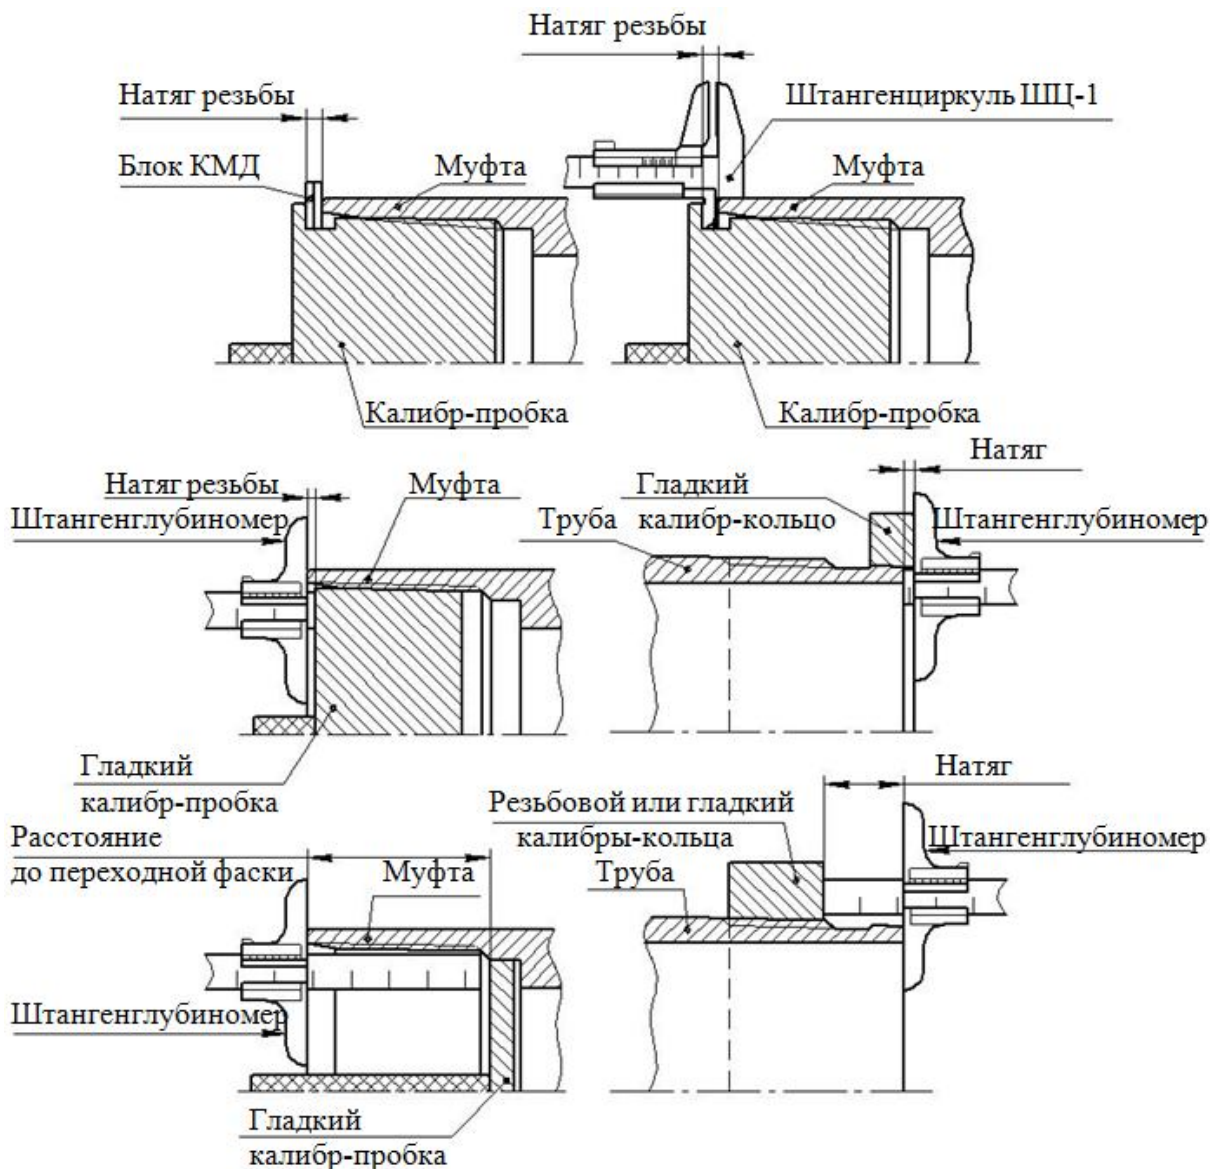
Схема измерения величины натяга резьбы трубы и муфты с трапецеидальной резьбой с узлом уплотнения «металл-металл»
